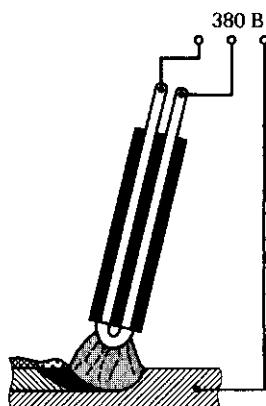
Схема сварки трехфазной дугой
